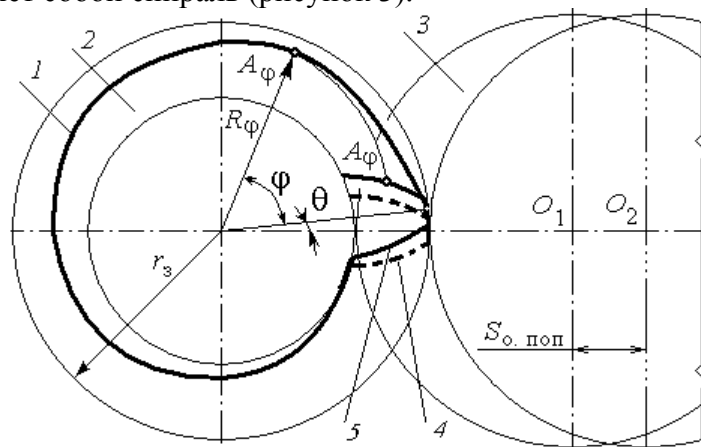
Траектория следа зуба накатника на заготовке: $r_з$ – радиус заготовки; R_ϕ – переменный радиус следа зуба накатника на заготовке; ϕ – угол, определяющий положение точки контакта; A_ϕ – точка контакта; θ – угол завала зуба; 1 – траектория следа зуба накатника на заготовке; 2 – заготовка; 3 – накатник; 4 – теоретической профиль; 5 – реальный профиль
